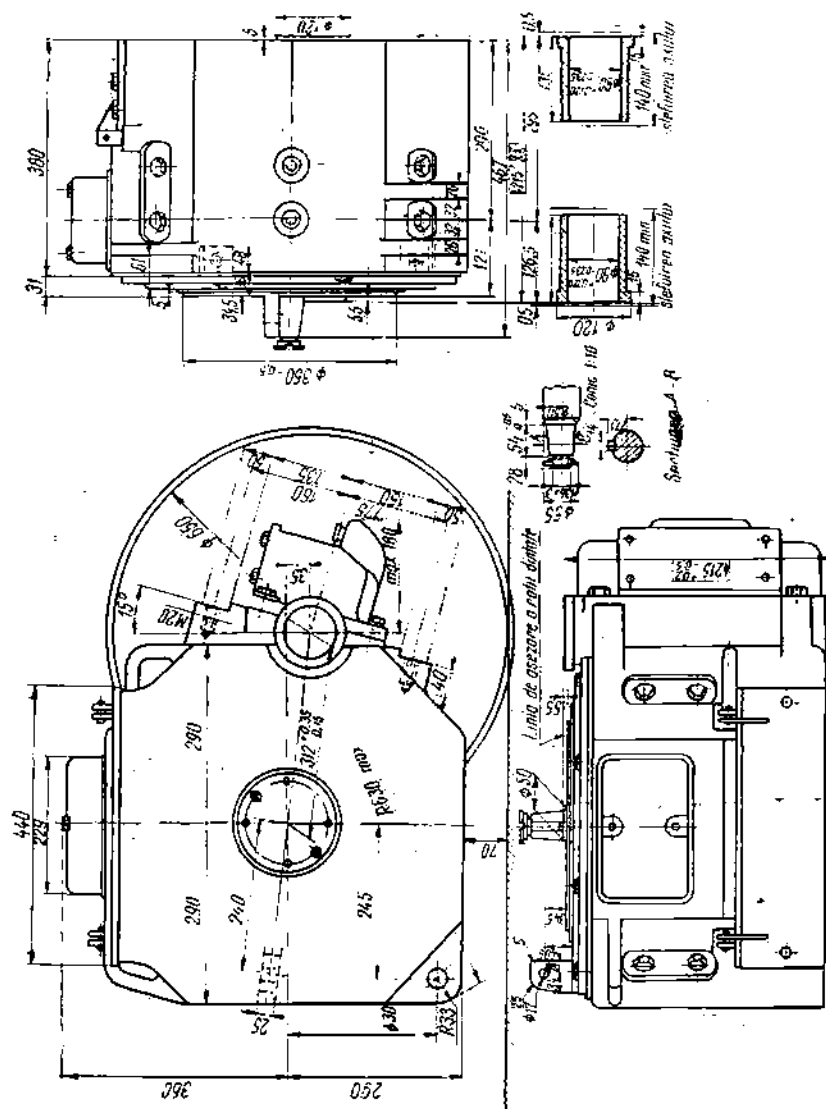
Motor tip SSTN. Dimensiuni de montaj.
